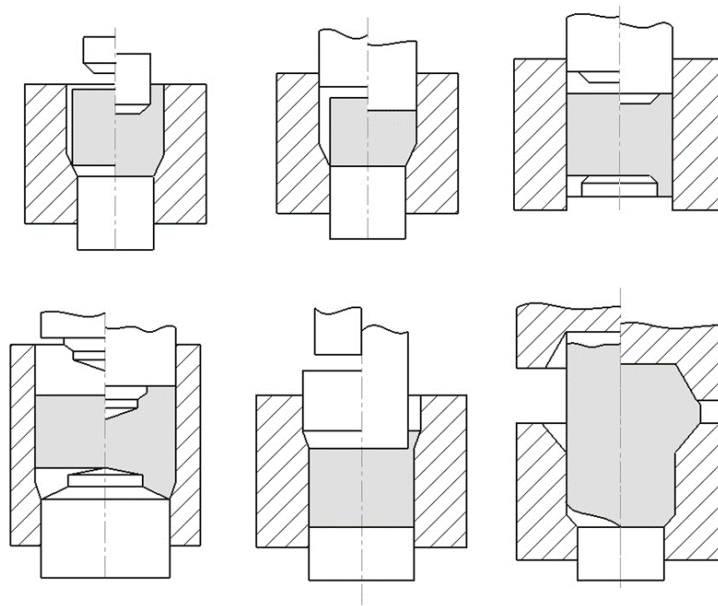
Схеми калібрування способами осадження заготовки [3]
